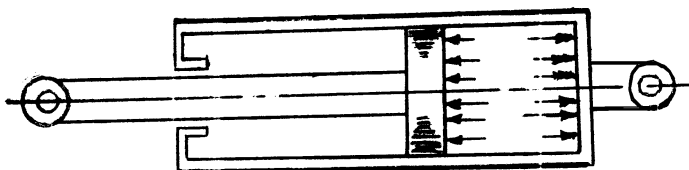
Пневматичний зрівноважувальний механізм
